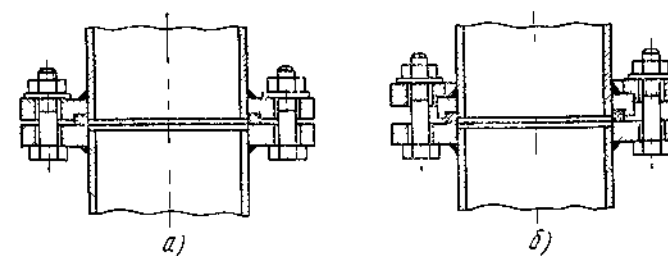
Схемы фланцевых соединений с резиновыми уплотнителями:
